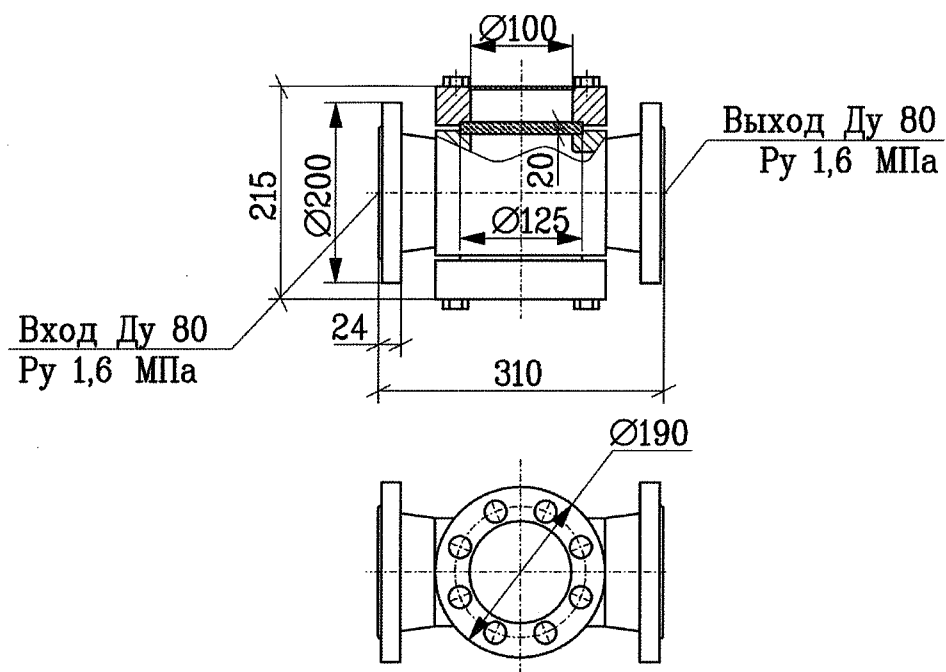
Габаритный чертеж фонаря смотрового LDP44AX001
